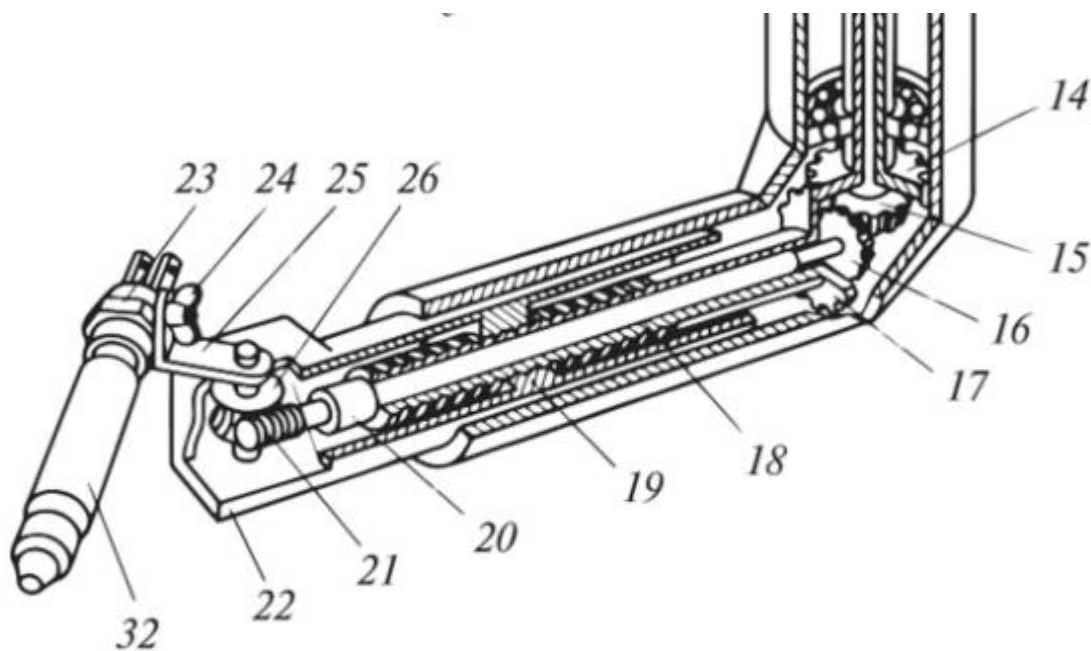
Манипулятор для токарно-карусельного станка с дистанционным регулированием положения плазматрона:
